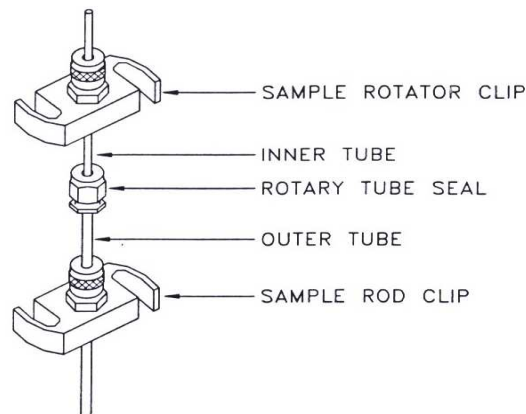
Parte superior do rotor. O “Sample rotator clip” é conectado a um motor de passo que promove rotações sobre um eixo vertical.
